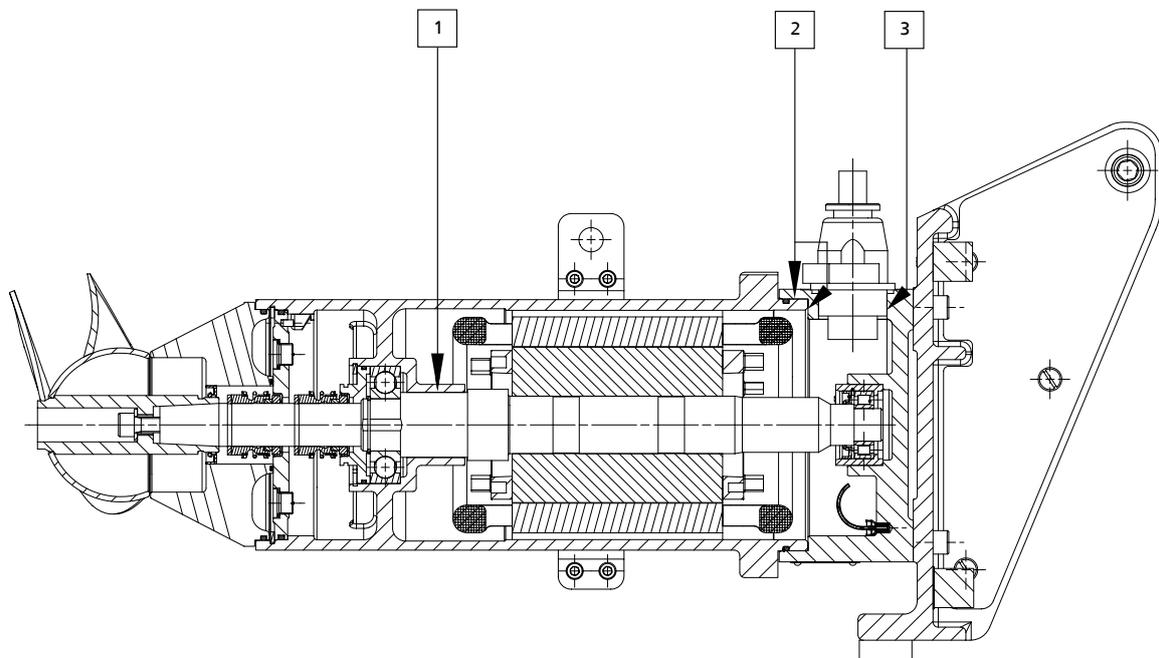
Ex-Spaltflächen bei explosionsgeschützten Motoren - Ausführung G
